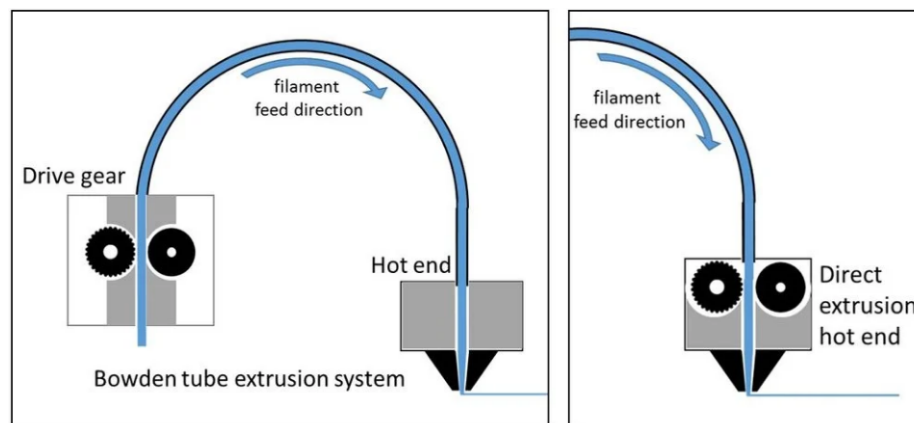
Diseño Bowden(izquierda) y Direct Drive(derecha) [28]
